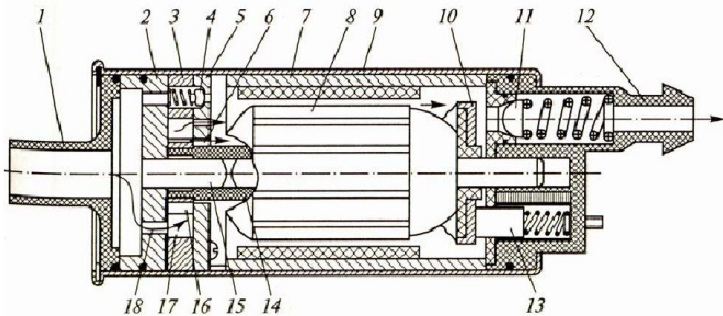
Електричний паливний насос: 1 – підвідний штуцер; 2 – основа; 3 – статор насоса; 4 – запобіжний клапан; 5 – кришка; 6 – вихідний канал; 7 – статор електродвигуна; 8 – якір електродвигуна; 9 – корпус; 10 – колектор; 11 – зворотний клапан; 12 – напірний штуцер; 13 – щітка; 14 – муфта; 15 – вал; 16 – сепаратор; 17 – ролик; 18 – вхідний канал
